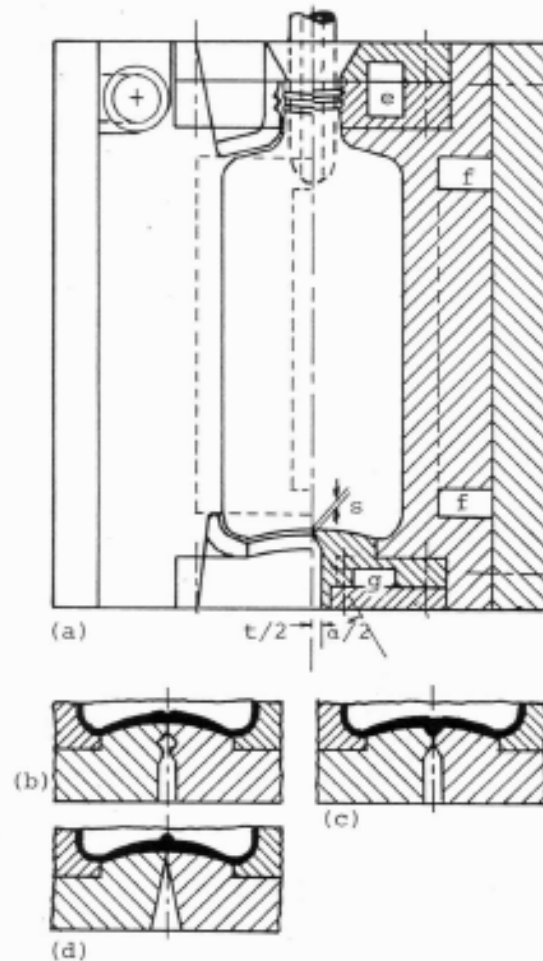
Vista em corte de um molde para a moldagem por sopros, mostrando a bolsa de esmagamento e a refrigeração do molde. a, b, c, d) diferentes concepções da bolsa de esmagamento; e, f, g) circuitos de refrigeração para o bocal, o corpo do moldado e o fundo do recipiente, respectivamente (Observar a decomposição em inserts, para simplificação dos processos de usinagem do molde). s - Largura da plataforma de esmagamento; a - Ângulo da bolsa; t - Largura da bolsa de esmagamento.
